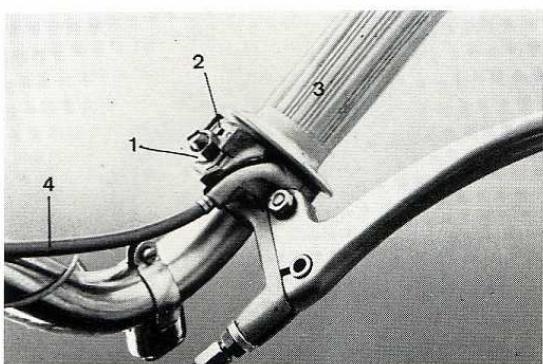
DEMONTAGE DE LA POIGNEE DES GAZ.
